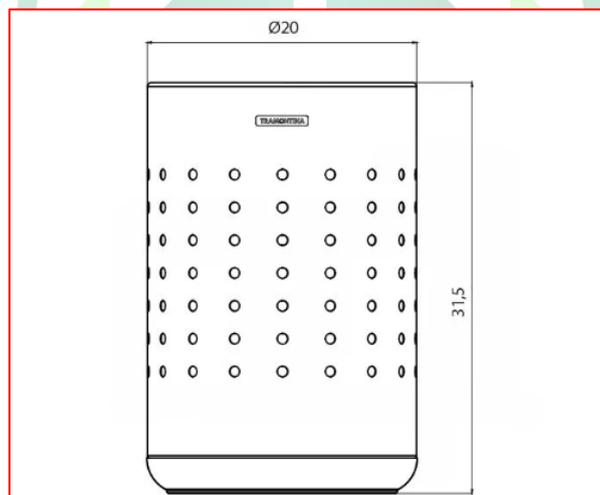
Cesto para papel metálico, 10l - Fonte: Tramontina
